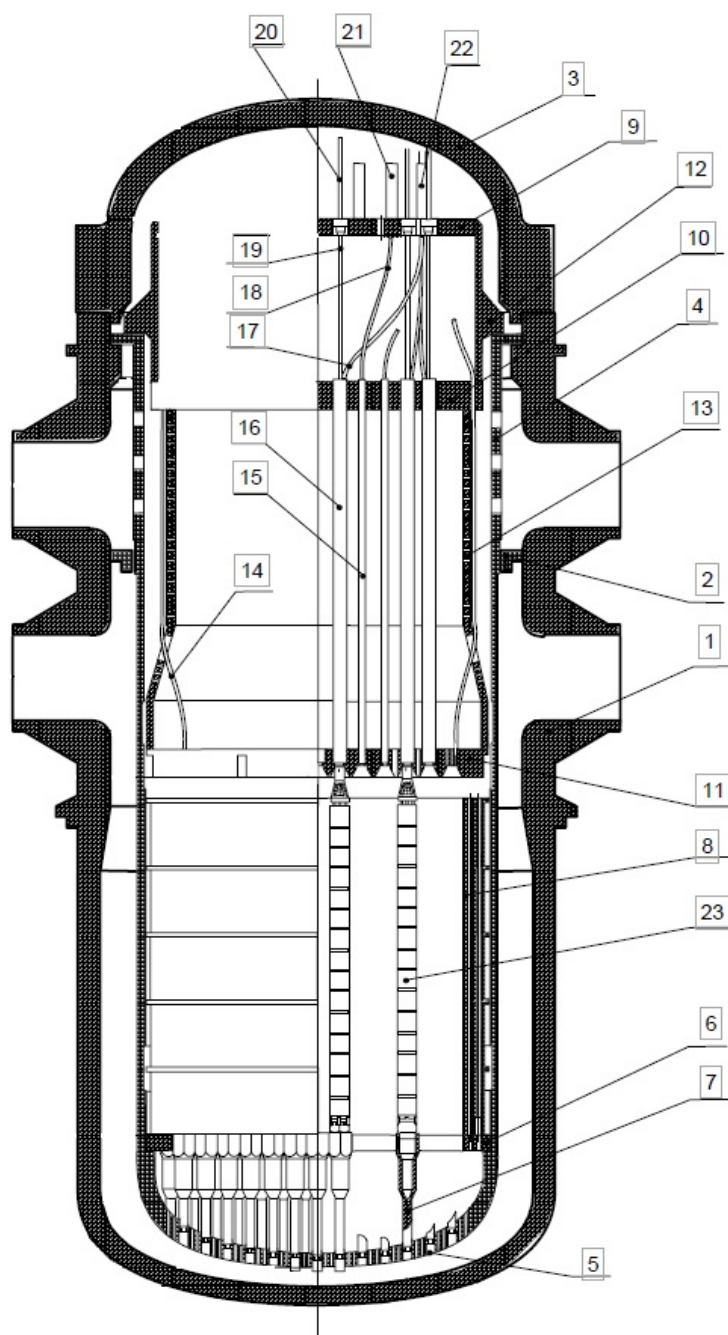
Реактор та основні внутрішньокорпусні пристрої.
